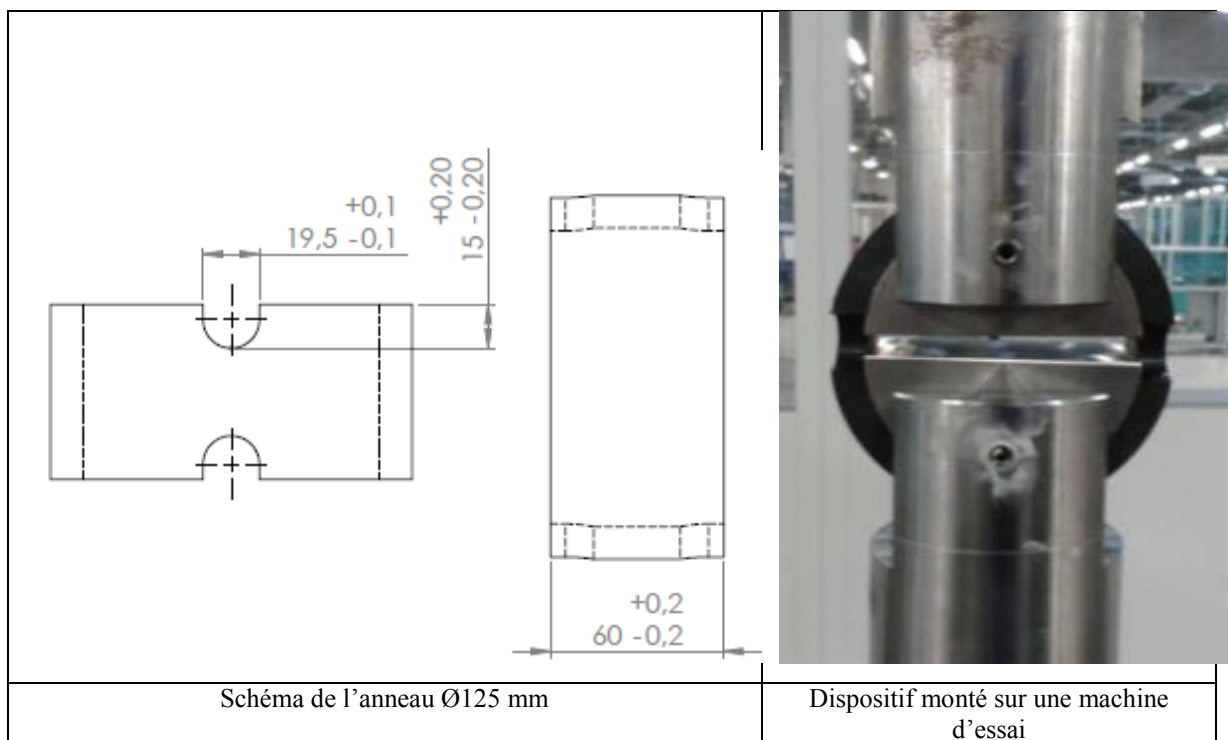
Géométrie des anneaux et dispositif monté sur une machine d'essai
